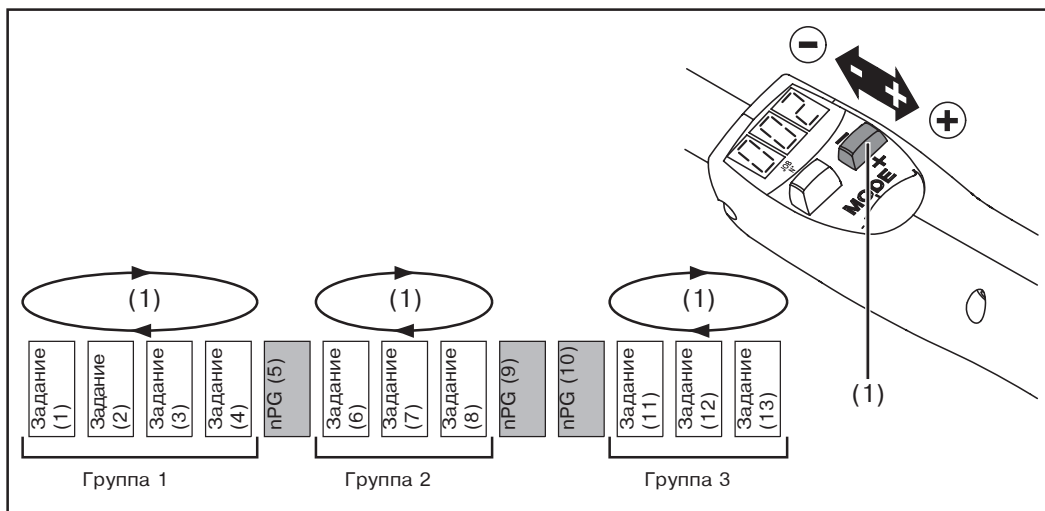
Вызов заданий с помощью сварочной горелки JobMaster TIG
